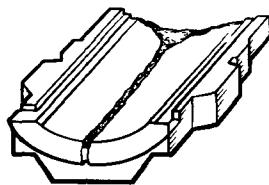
Подшипник с разошедшейся трещиной в баббитовом слое
